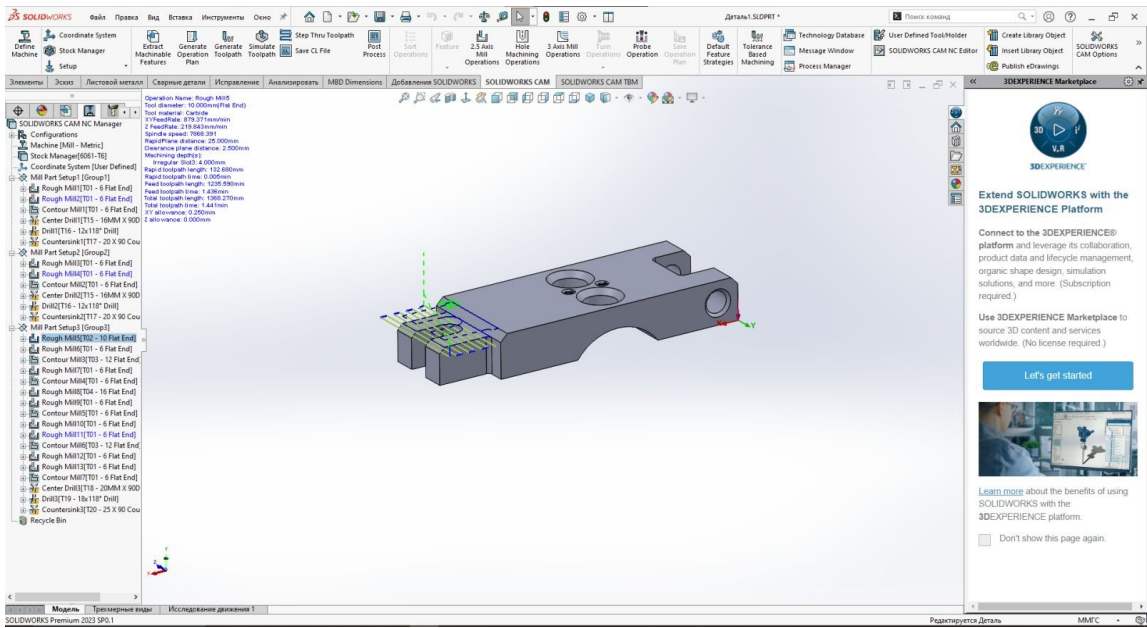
Траекторія обробки - фрезерування верхньої площини
